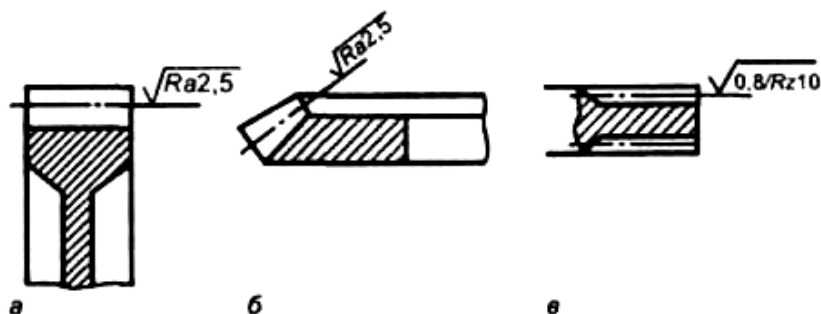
Обозначение шероховатости поверхностей зубьев зубчатых колес
